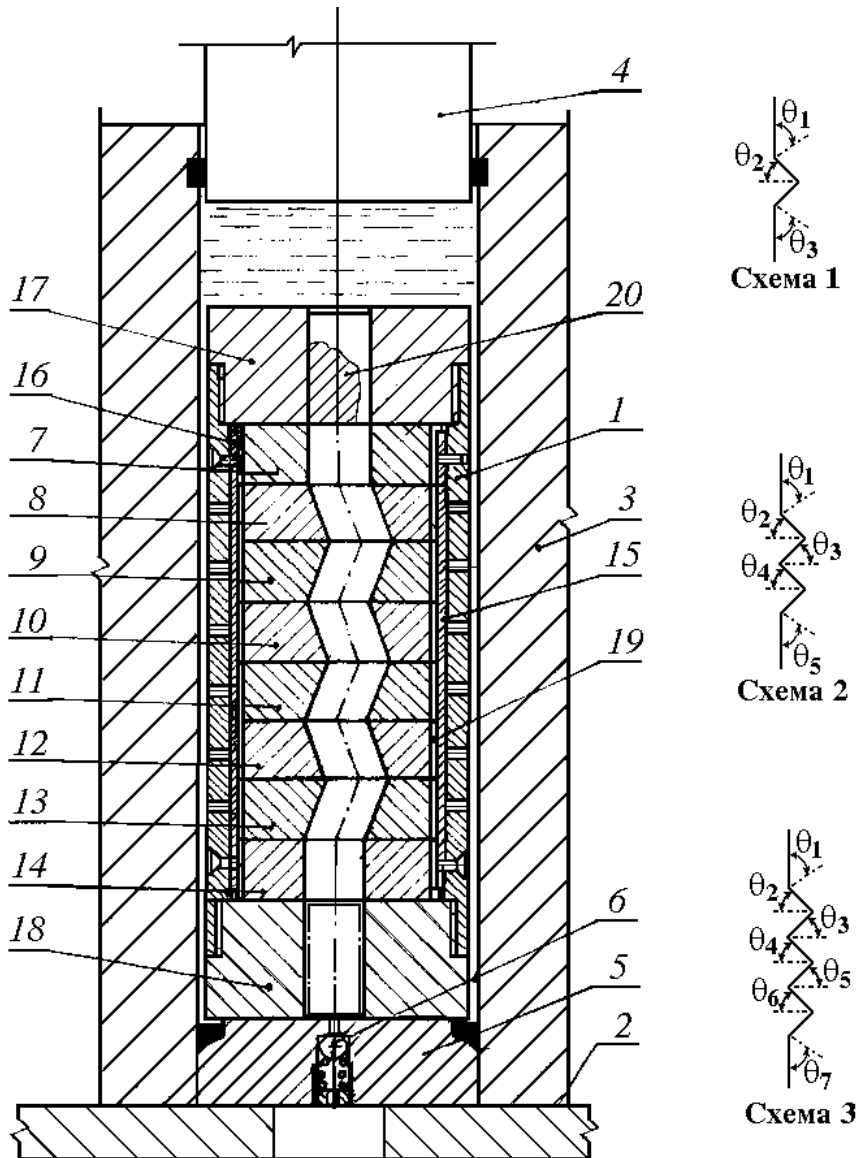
Деформирующий блок и схемные варианты его выполнения: 1 – компакт-блок; 2 – траверза пресса; 3 – контейнер; 4 – пуансон; 5 – матрицедержатель; 6 – перепускной клапан; 7–14 – втулки; 15, 16 – шпонки; 17, 18 – опорные элементы; 19 – шпоночный паз; 20 – заготовка
